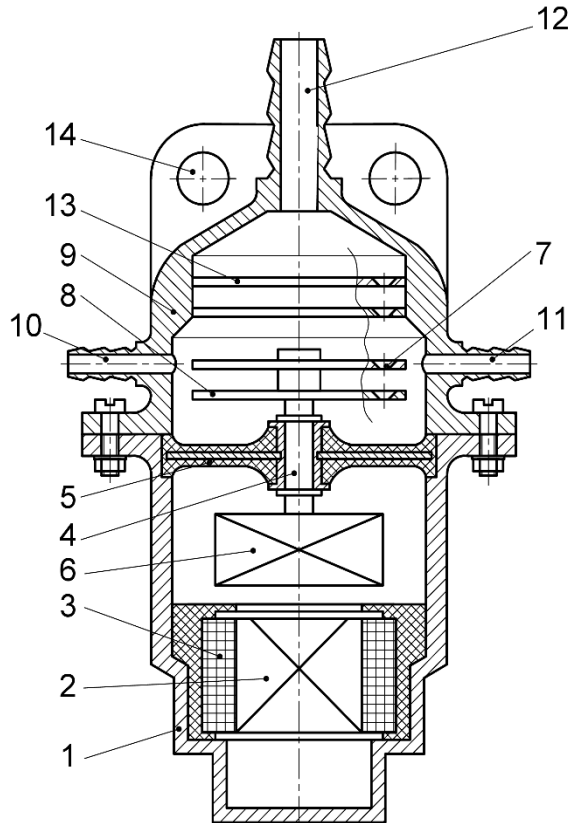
Принципова конструктивна схема кавітаційного віброзмішувача для підготовки водяно-бензинової паливної суміші двигуна електрогенератора
